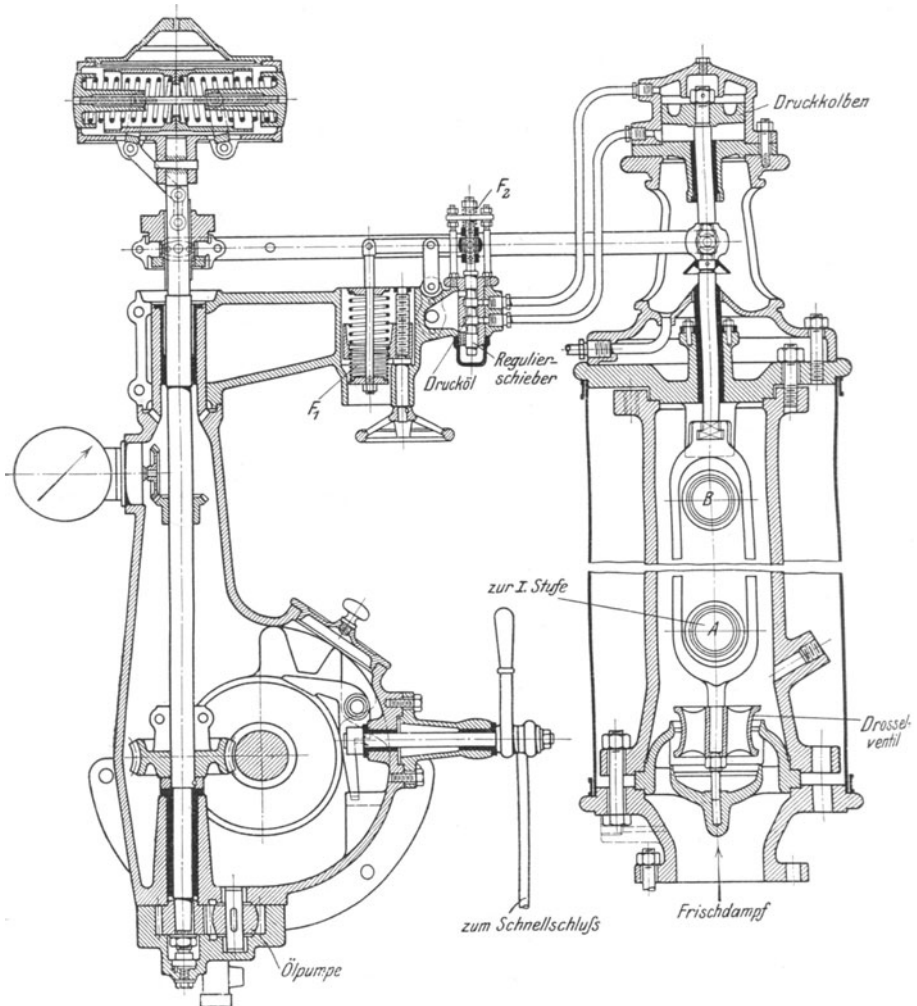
Regulator mit Druckölsteuerung für den Dampfteinlaß in die Turbine.
